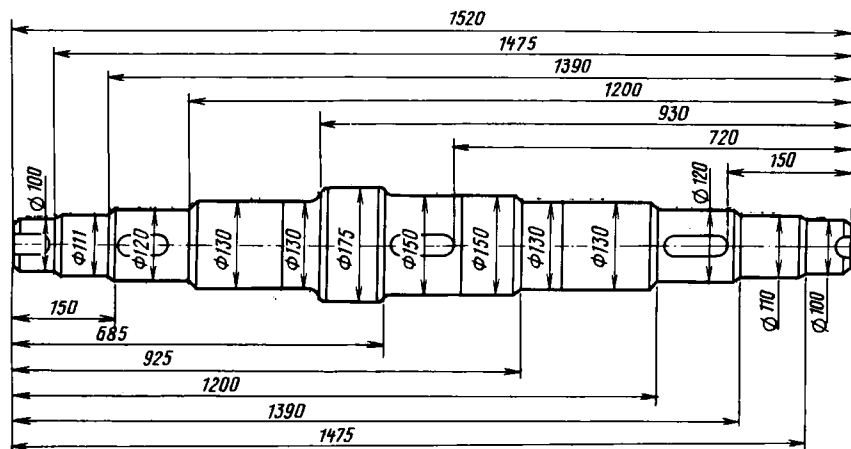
Главный вал эскалатора ЛП-6ИО-6И
